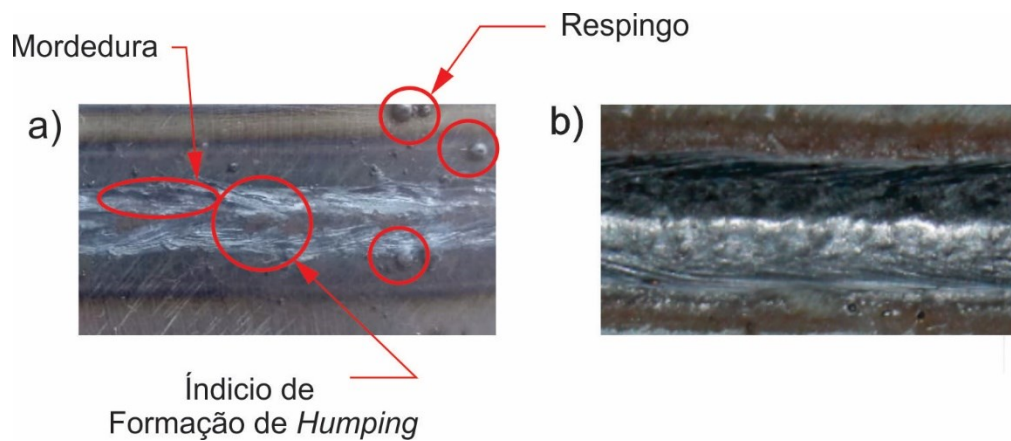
Aspectos das superfícies dos cordões de solda obtidos pelos processos de soldagem LBW (a) e HLAW (b), destacando a formação de defeitos na soldagem Laser.
